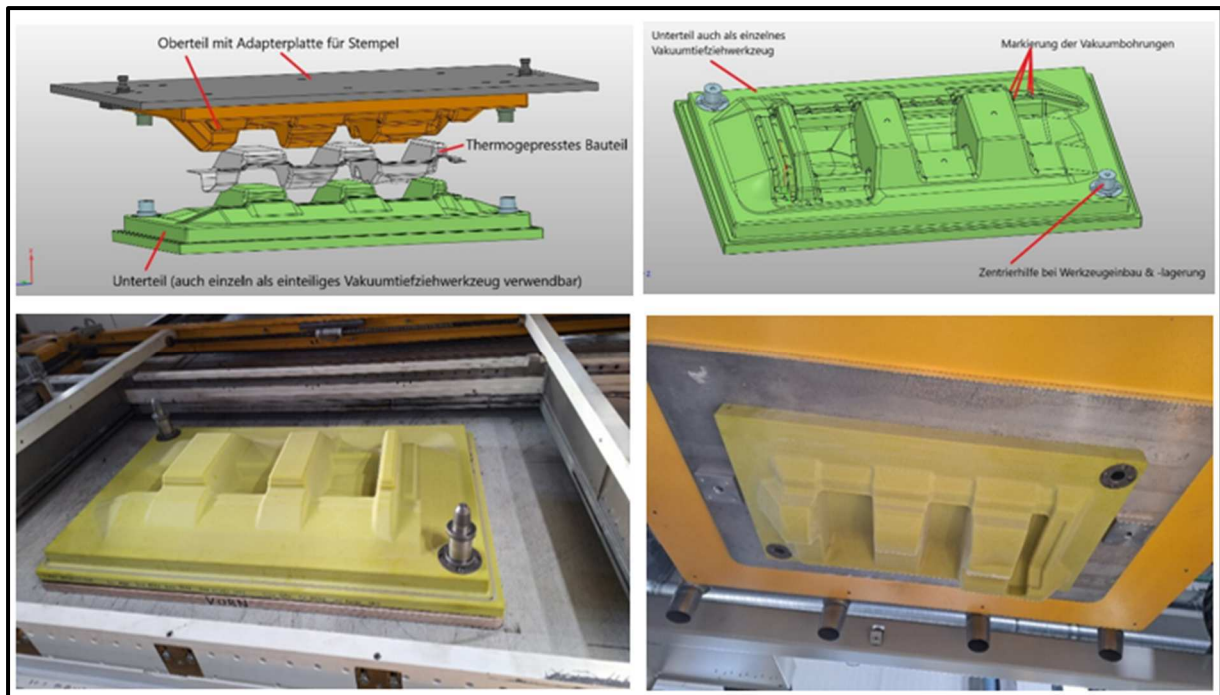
Aufbau Testwerkzeug / 25.01.24 Lakowa intern.
